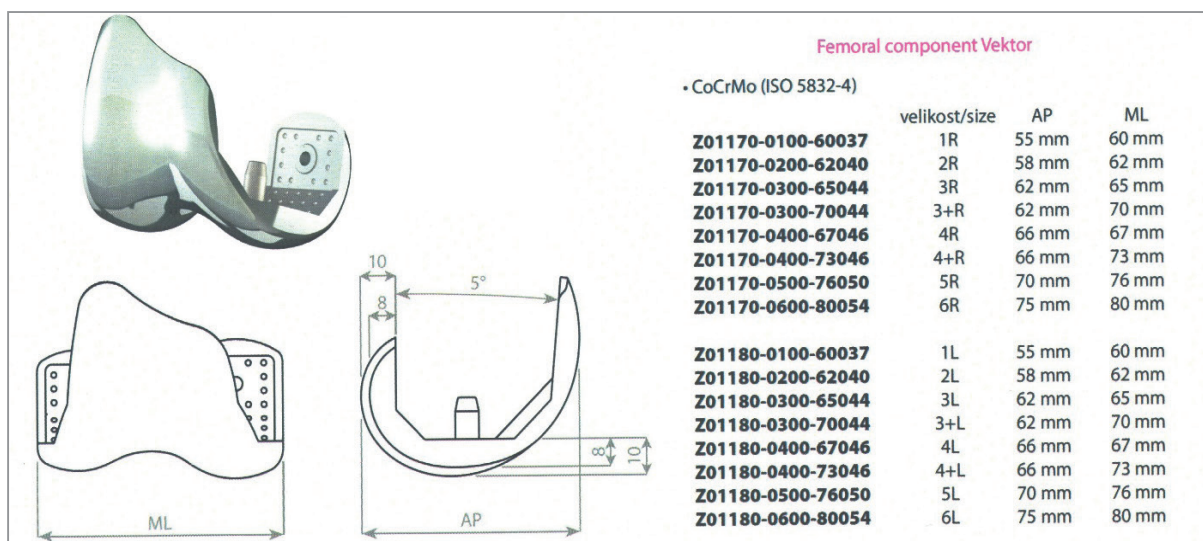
Типоразмер верхней части имплантатов коленного сустава
